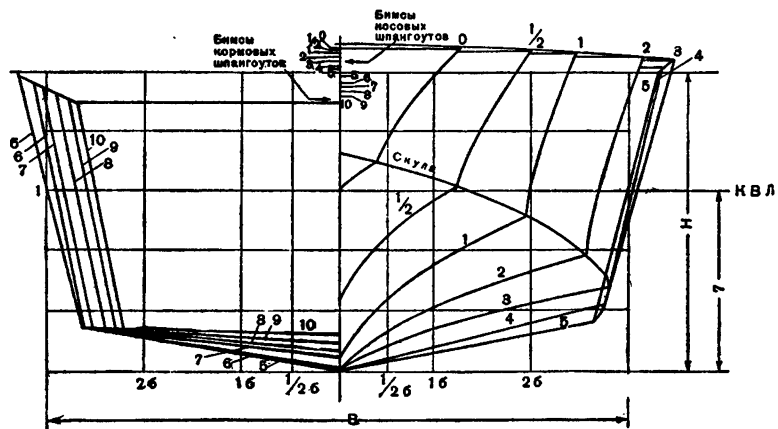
Чертеж теоретического корпуса модели спортивного катера.
